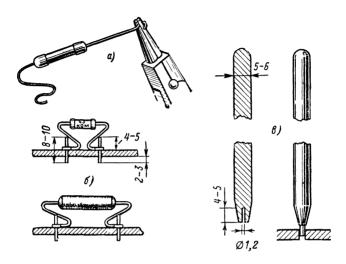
Монтаж деталей на шпильках и приспособление для запрессовки шпилек.
